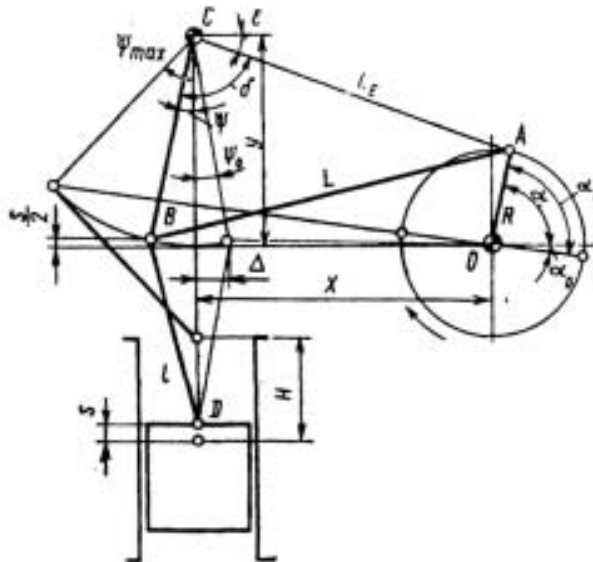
Кинематическая схема коленно-рычажного механизма пресса
